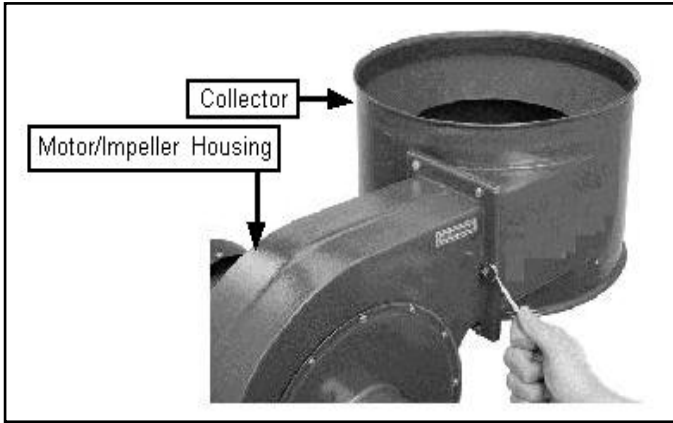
Installation du collecteur sur le carter du moteur/de la turbine.
